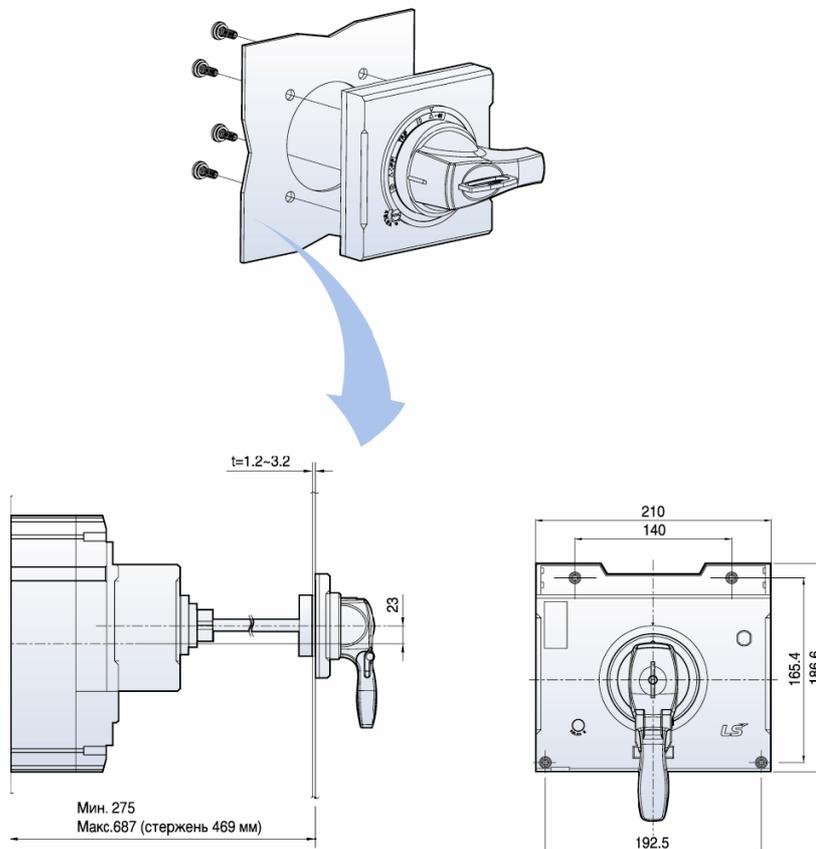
Габаритные и установочные размеры, способ установки выносных поворотных рукояток TS400 и TS630
